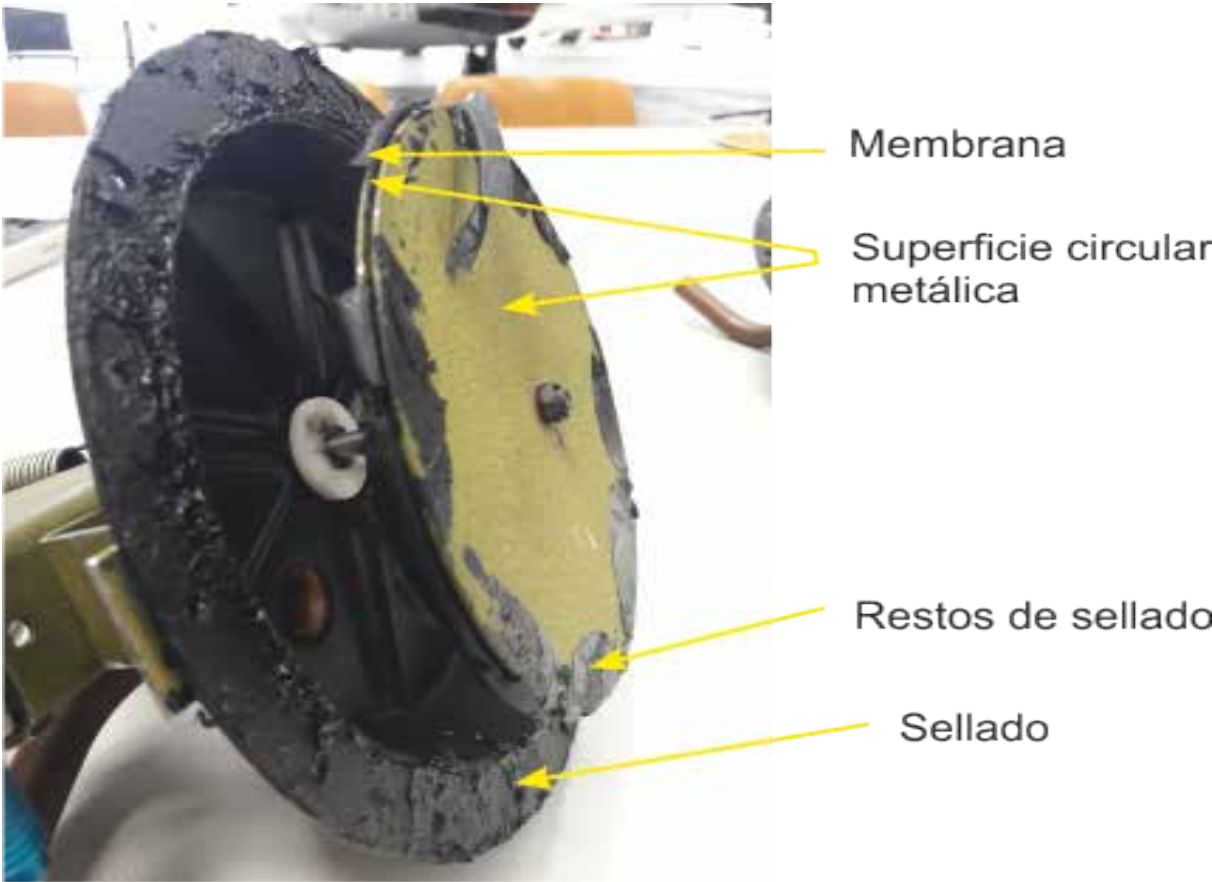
Conjunto diafragma despegado de carcasa
